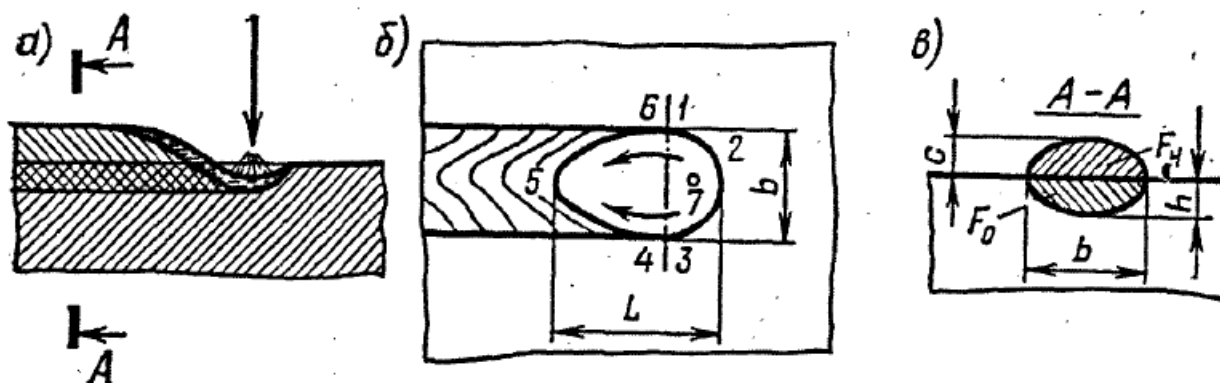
Зварювальна ванна. Кристалізація металу при зварюванні та формування металу шва
